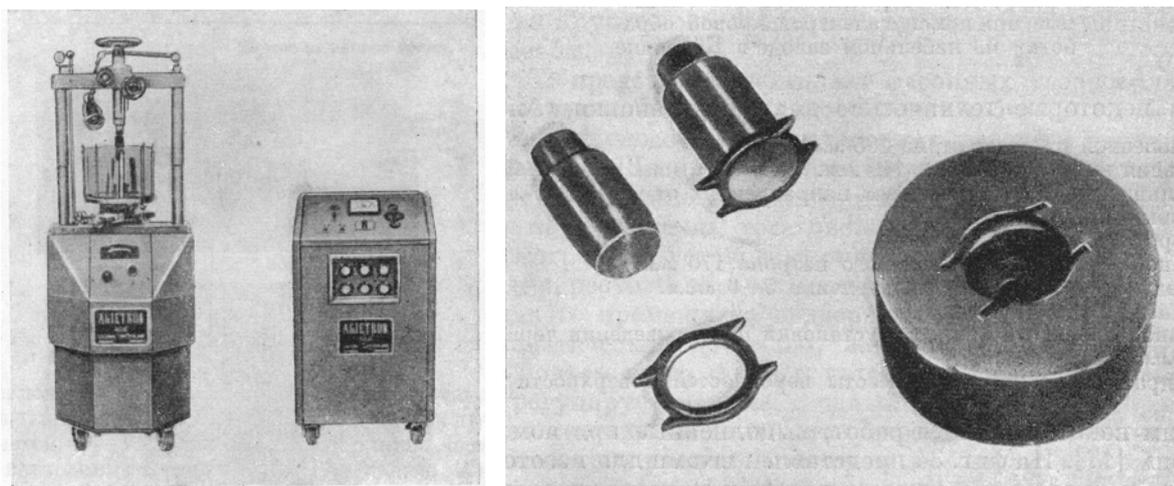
Внешний вид электроискровой установки «Ажитрон» и изготовленный на этой установке штамп для корпуса часов и электроды, при помощи которых он изготовлялся
